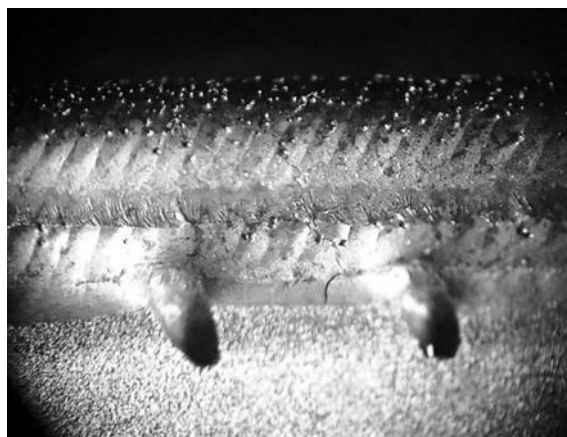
Вид трещины в наплавке рабочей лопатки первой ступени ТВД
